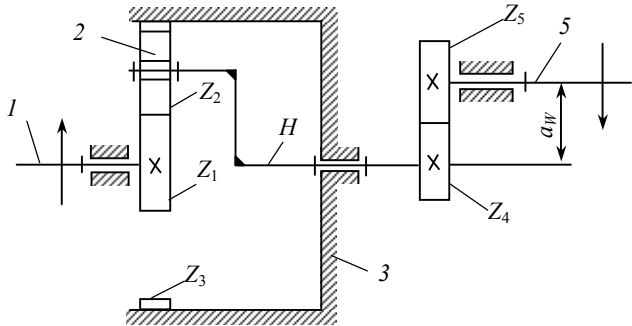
Схема редуктора промежуточного привода авиационного двигателя
